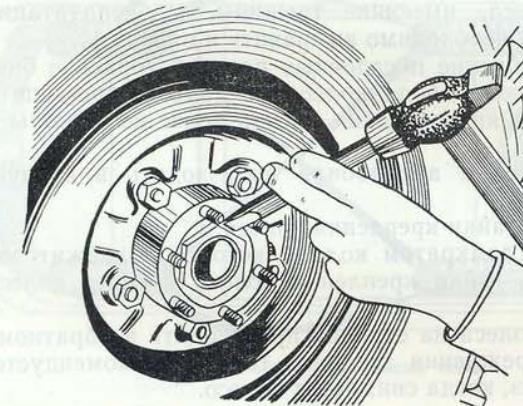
Стопорение гаек подшипников ступицы колеса ведущего моста
